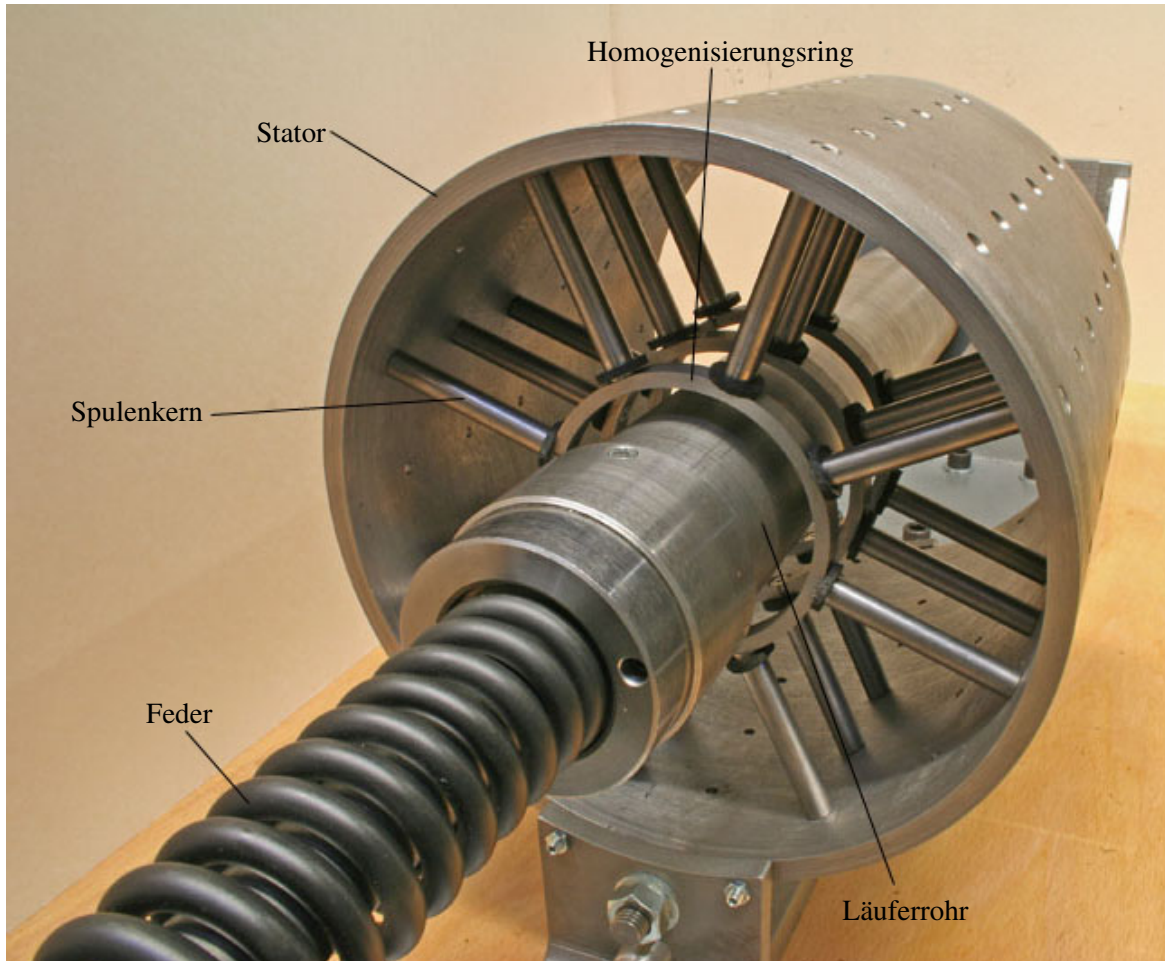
Mechanischer Gesamtaufbau des Prototypen.
